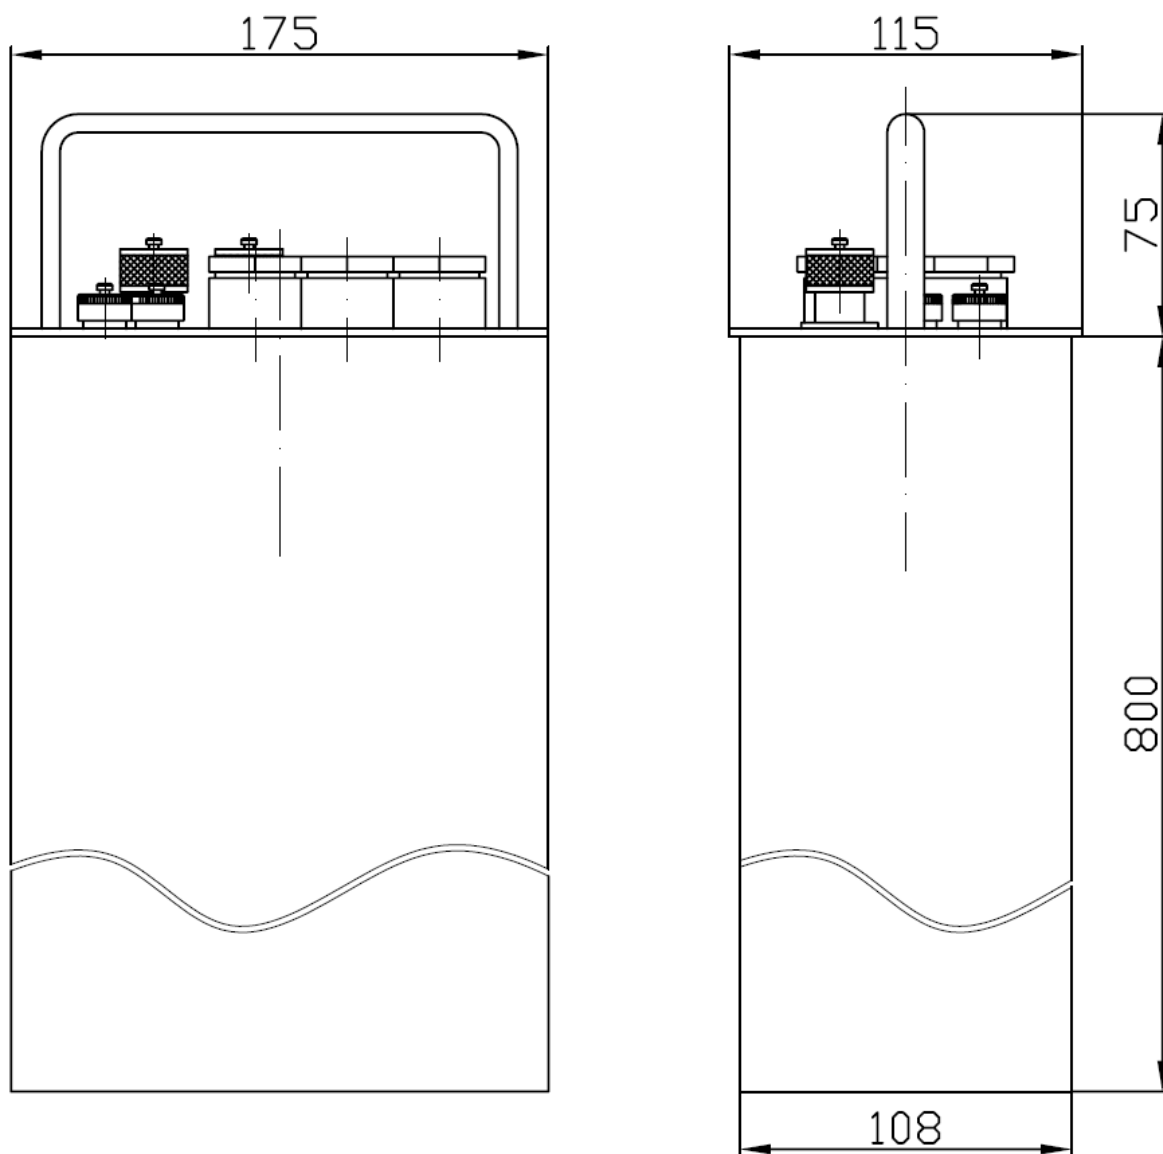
Корпус MGS-3-CASE-ST-BK300, вид сбоку
